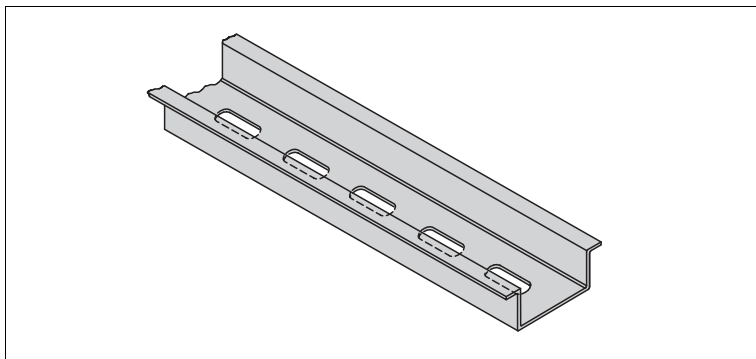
Exemple : rail de montage DIN UPR-MR (35 mm x 15 mm)
